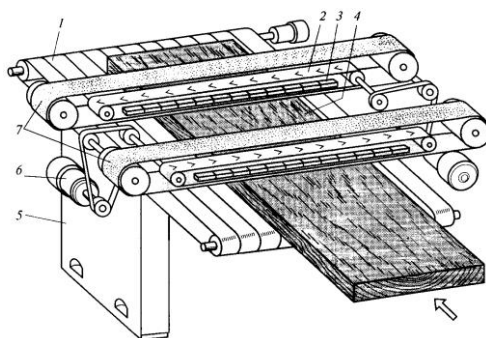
Схема двострічкового шліфувального верстата з конвеєрною подачею: 1 – стрічковий конвеєр; 2 – опорна стрічка; 3 – контактна балка; 4 – деталь; 5 – станина; 6 – електродвигун; 7 – шліфувальні стрічки
